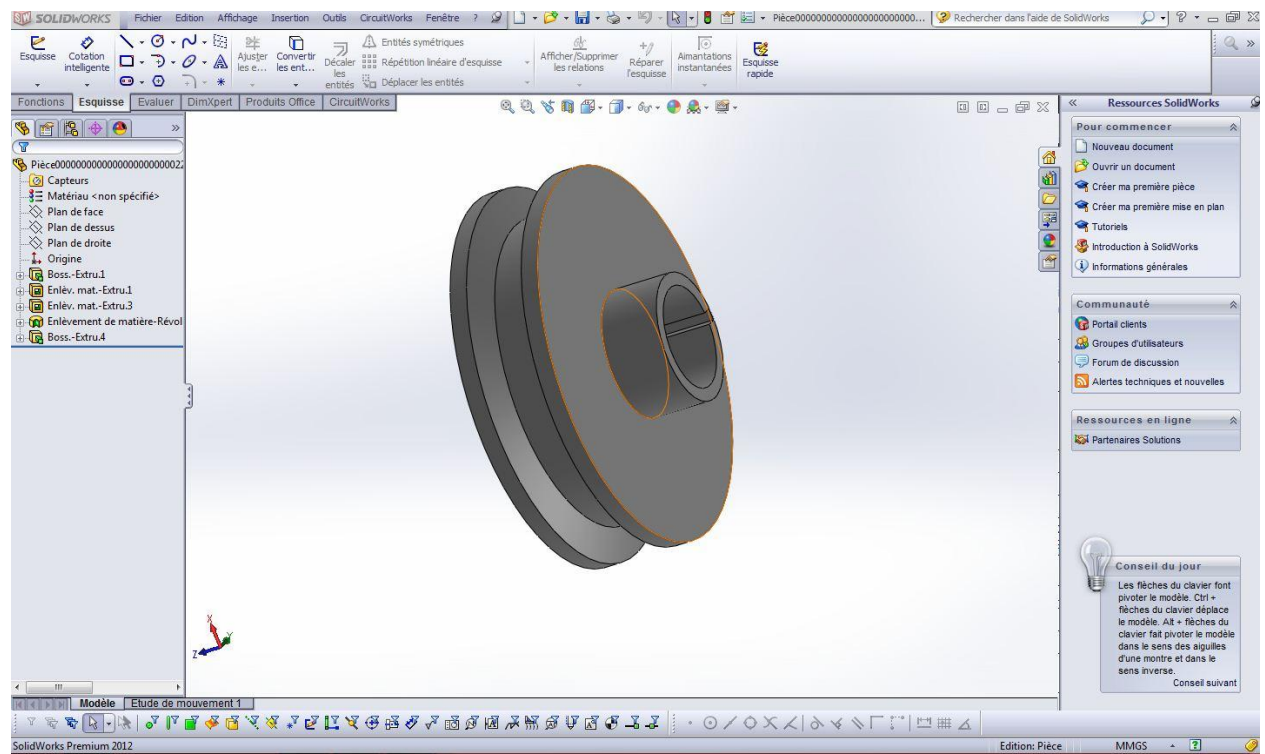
Vue de Poulies réalisée sous SOLIDWORKS
